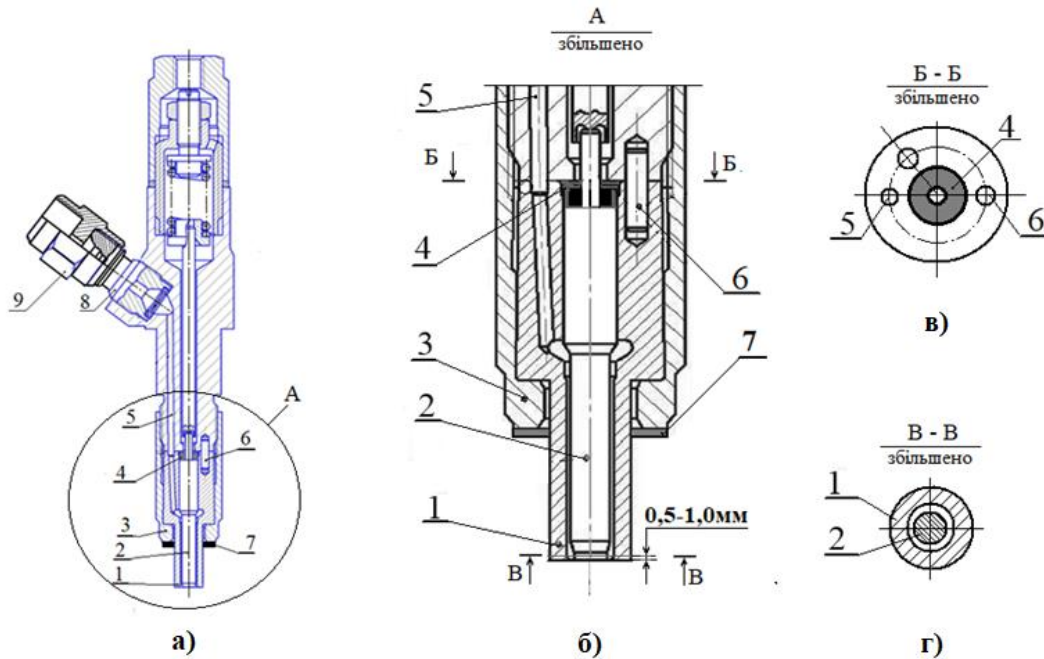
Адаптер з фальш розпилювачем: а) конструктивна схема адаптера з фальш – розпилювачем (адаптер у зборі); б) установка фальш – розпилювача на корпусі форсунки; в) вигляд фіксуючого і герметизуючого елемента; г) вигляд каналу для проходження повітря:
